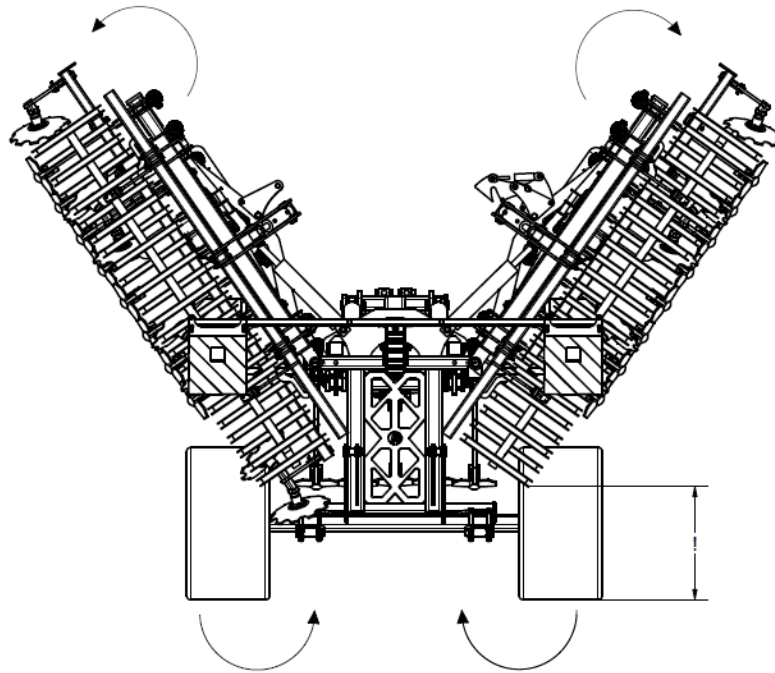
Séquence d'ouverture de la machine : ouverture de la machine avec une attention particulière à la hauteur des extrémités des porte-bras par rapport au sol.
